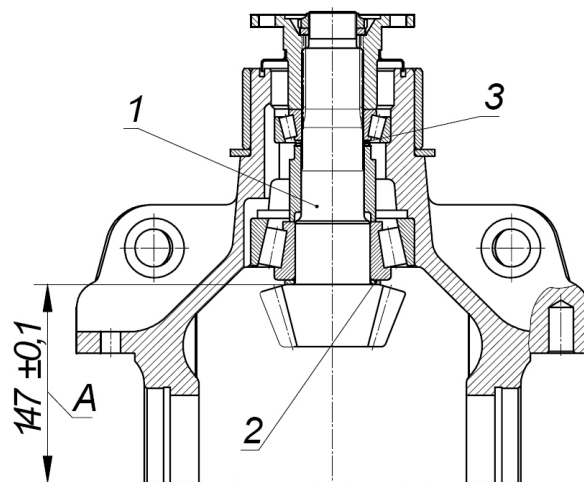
Ведущая шестерня в корпусе центрального редуктора:
